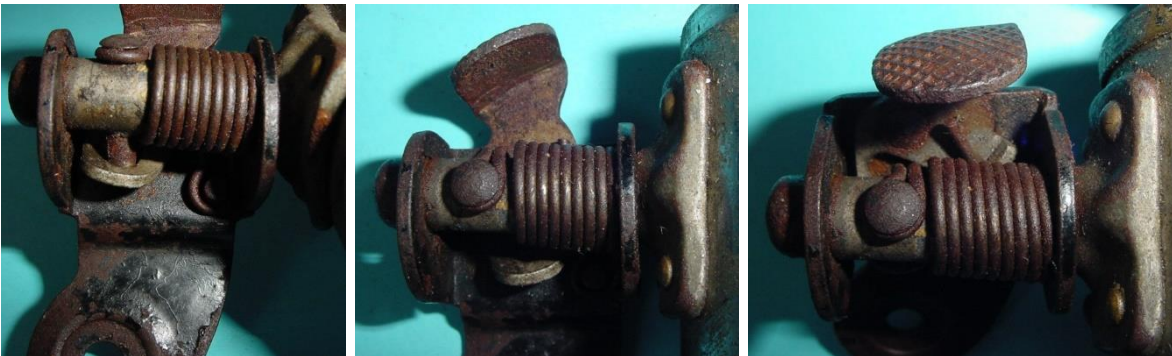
Befestigung des einteiligen Flansches Gestaltung mit vier Nieten
